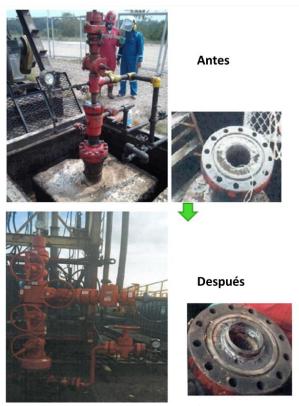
Ejemplo de soldadura de la extensión de revestimiento sobre la sección A del cabezal. Fuente. Operaciones de conversiones, Campo Llanito.
